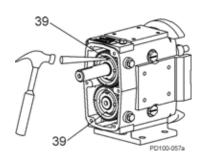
Pliage d'une languette de blocage sur les rondelles de blocage
